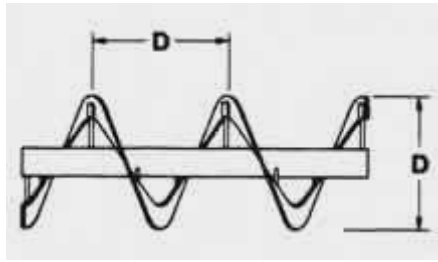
Tornillo de cinta simple. Fuente: <http://www.kwsmfg.com/services/screw-conveyor-engineering-guide/conveyor-flight-pitch-types.htm>
